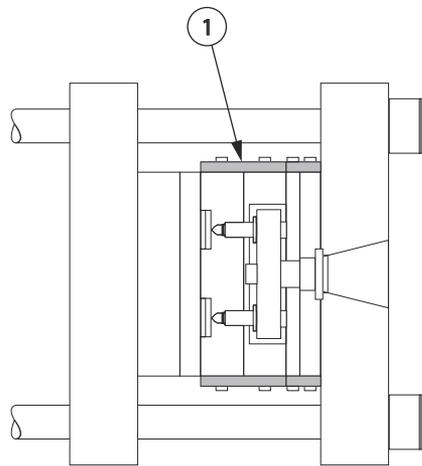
Arretieren der Kavitätenplatte am Heißkanal (Draufsicht)
